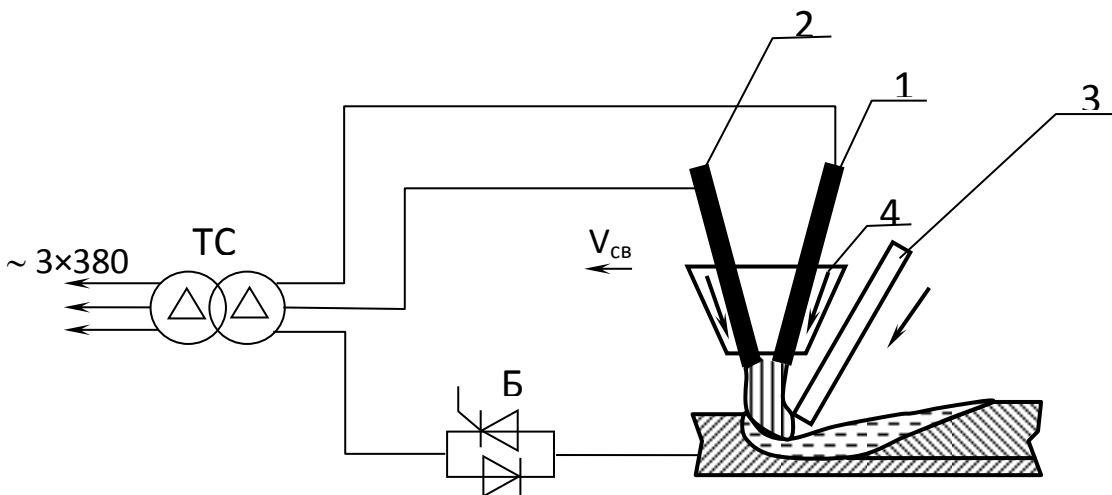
Схема сварки трехфазной дугой
